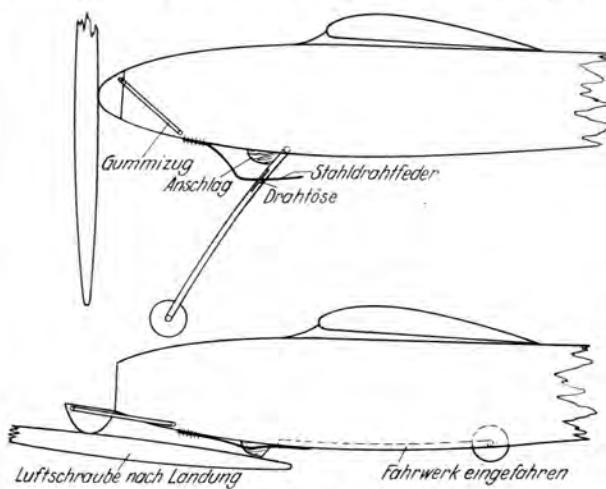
Aufbau und Wirkungsweise eines einklappbaren Einbeinfahrgerüstes.
